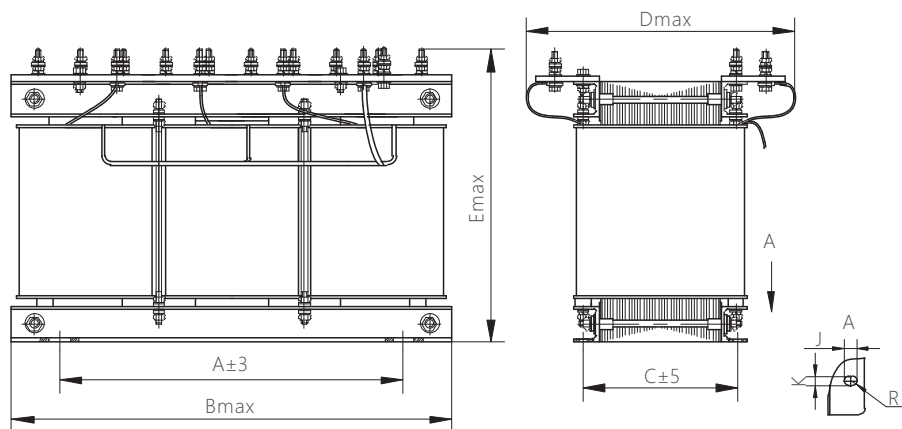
SCBK-8~20开启式外形尺寸与安装尺寸示意图
